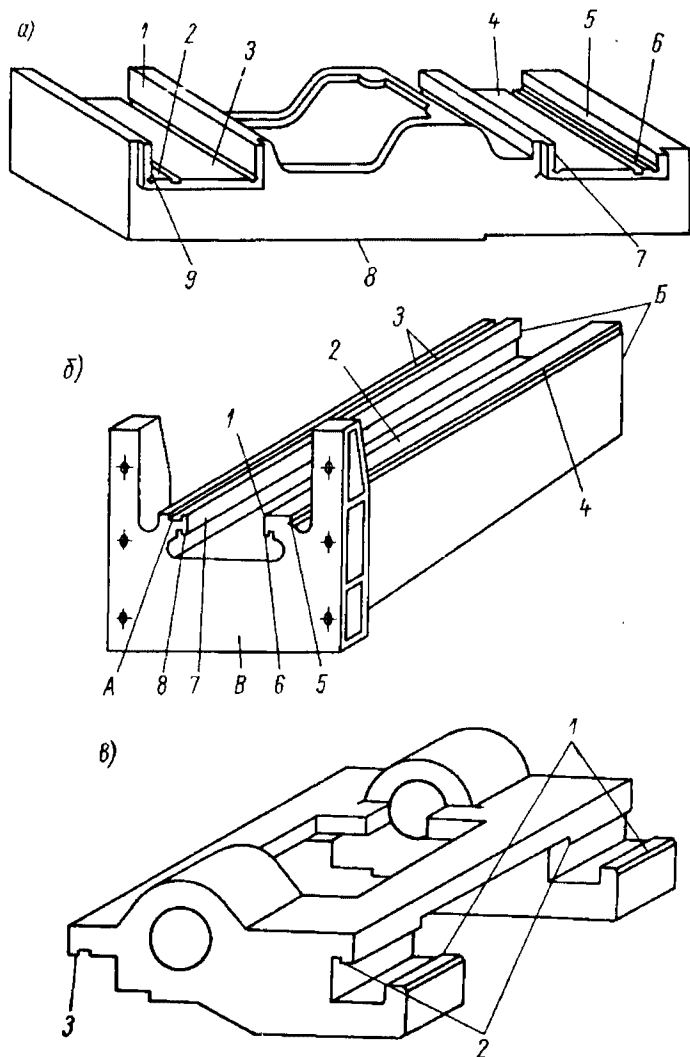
Корпусные детали задней стойки: а — каретка; б — стойка; в — корпус люнета
